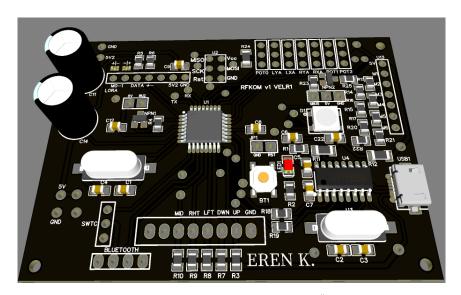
Alıcı Kartı PCB Çizimi (Arka Yüz)
